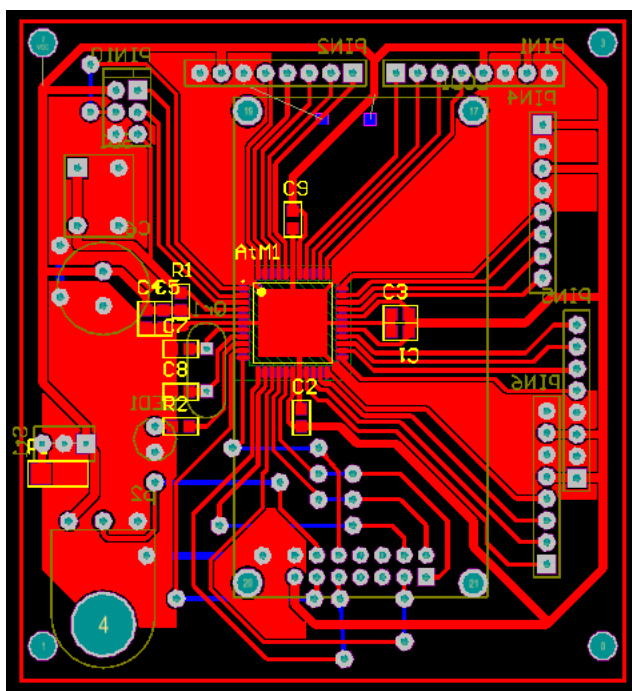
чертеж электрической схемы базового модуля выполненный в САПР
